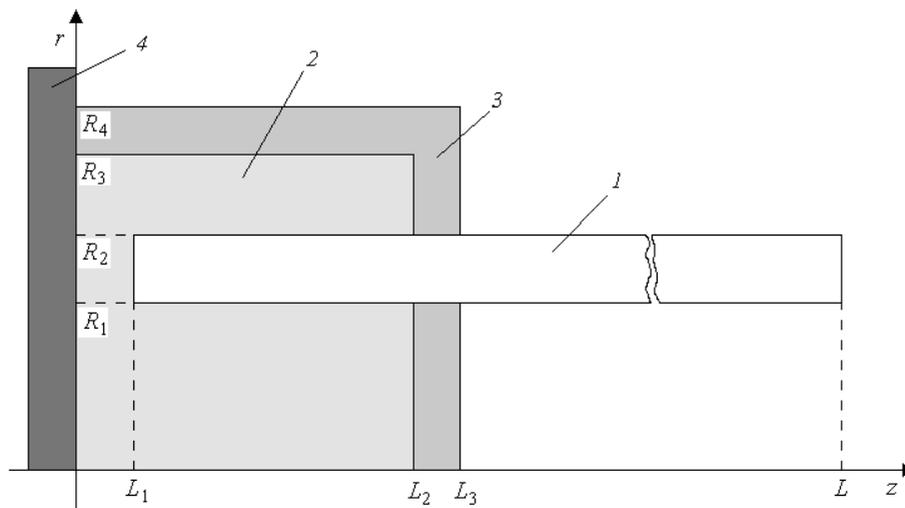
Расчетная схема подогрева стенки трубы: 1 — стенка трубы; 2 — сменная насадка для подогрева; 3 — слой теплоизоляции; 4 — нагревательная пластина сварочного аппарата
